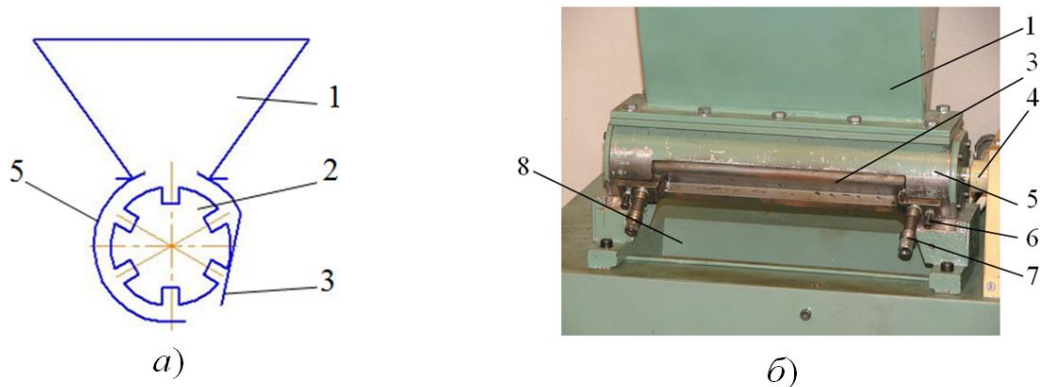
Схема (а) та загальний вигляд (б) дозатора вальцьової плющилки насіння олійних культур: 1 – завантажувальний бункер; 2 – живильний барабан; 3 – поворотний клапан; 4 – муфта; 5 – корпус; 6 – регулювальний гвинт; 7 – демпферний механізм; 8 – напрямний лоток.
